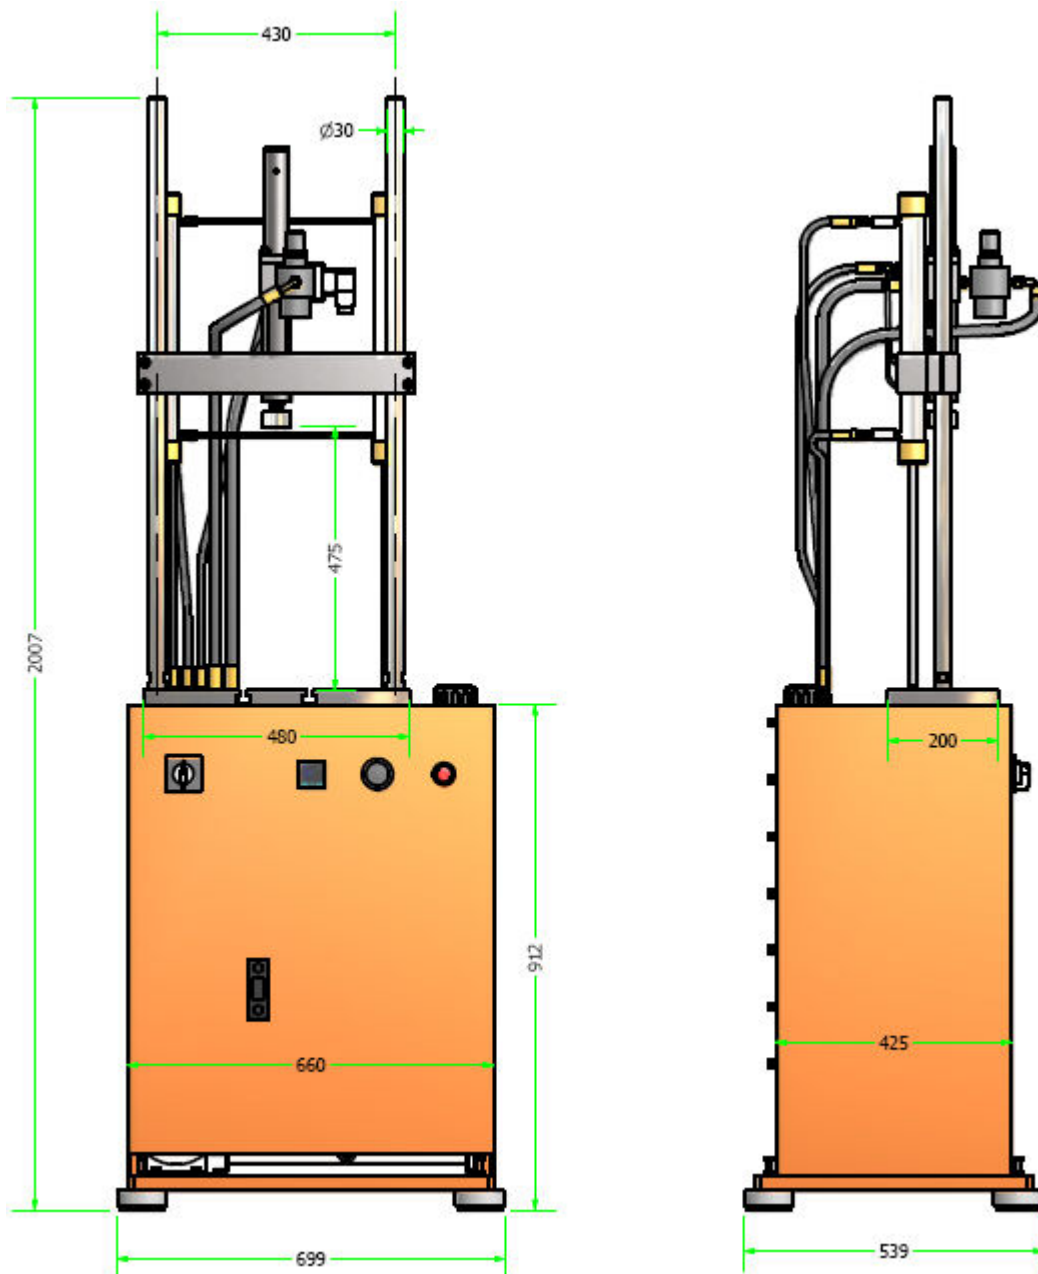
Dimensões principais da máquina de ensaio de 500 kg
